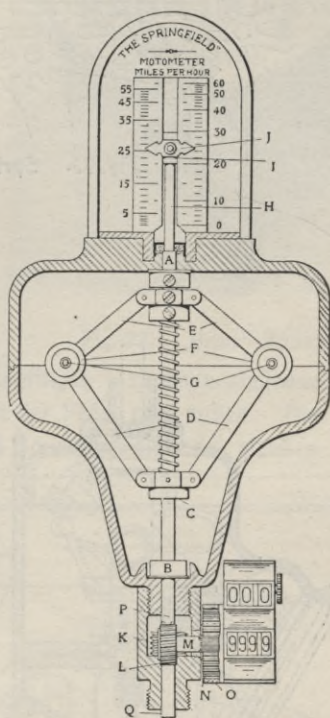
Innen-Ansicht des Springfield-Motometers.
